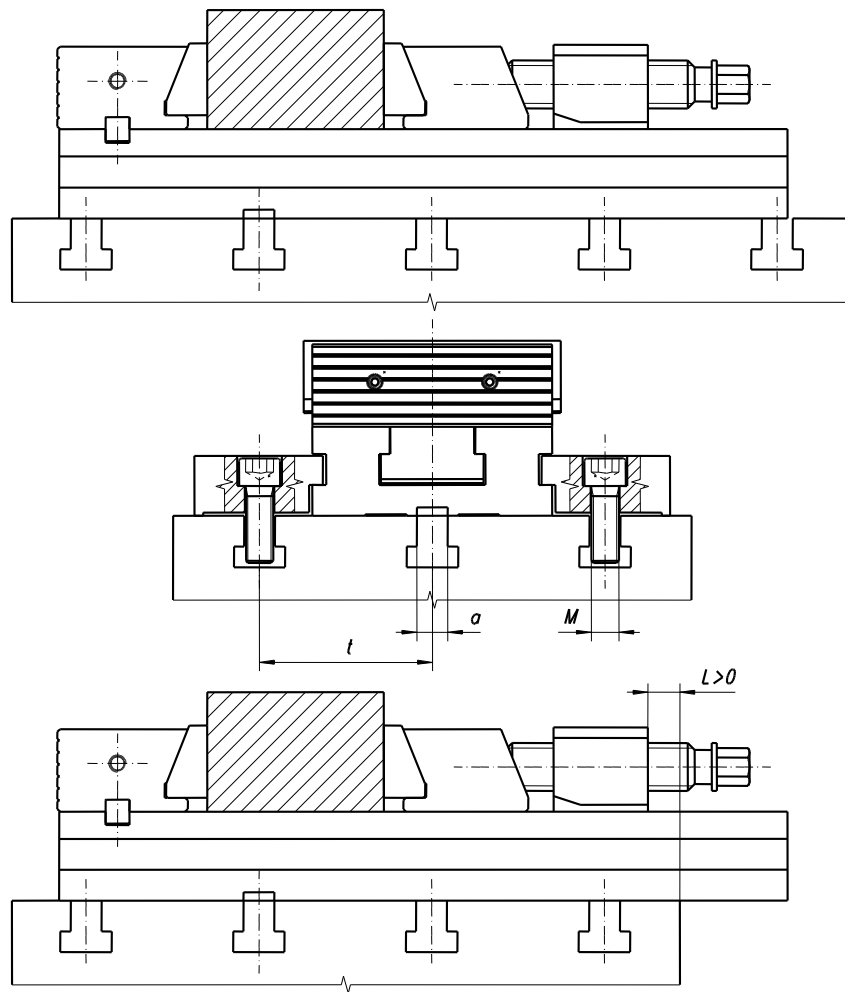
Richtige Lage des Schraubstocks auf dem WM-Tisch.
